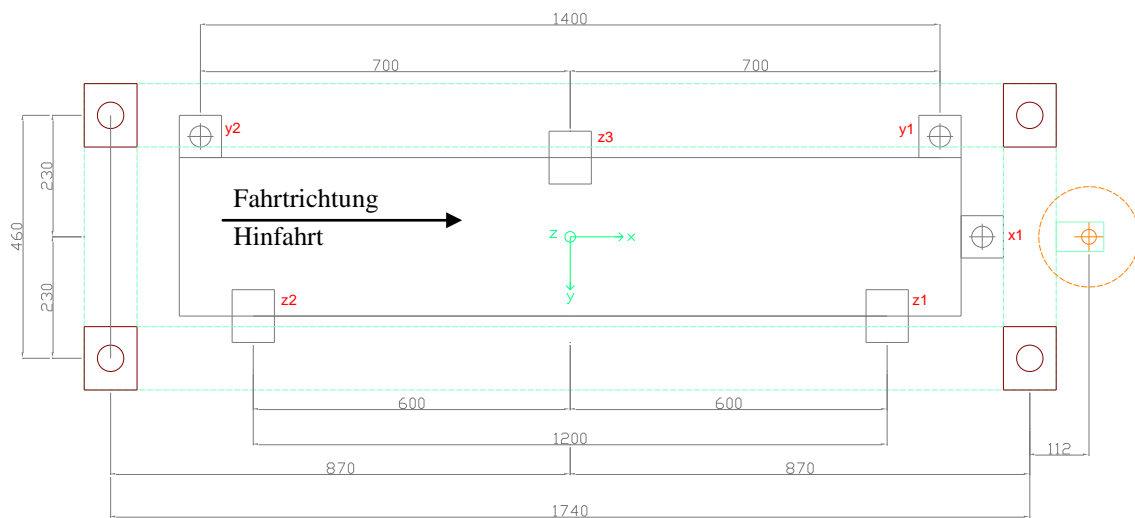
Draufsicht einer Prinzipskizze des Sechskomponenten Kraftmessgerätes im CEHIPAR Schleppkanal.
